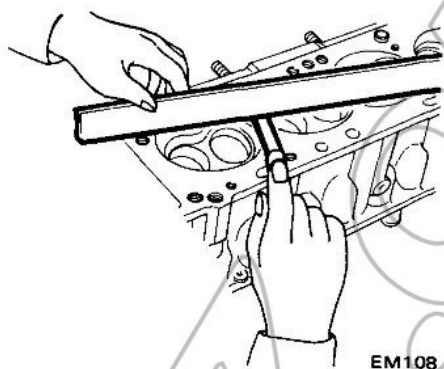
Contrôle de la planéité du plan de joint de culasse
